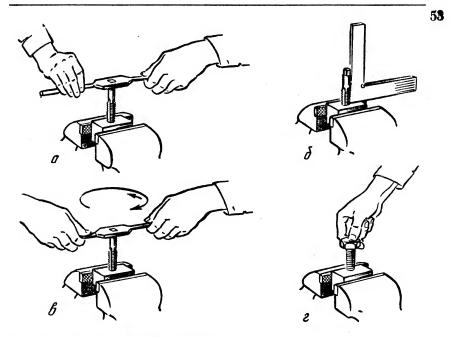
Нарезание резьбы метчиком: а — установка метчика; б — проверка угольником установки метчика; в — нарезание резьбы; г — проверка качества резьбы.
